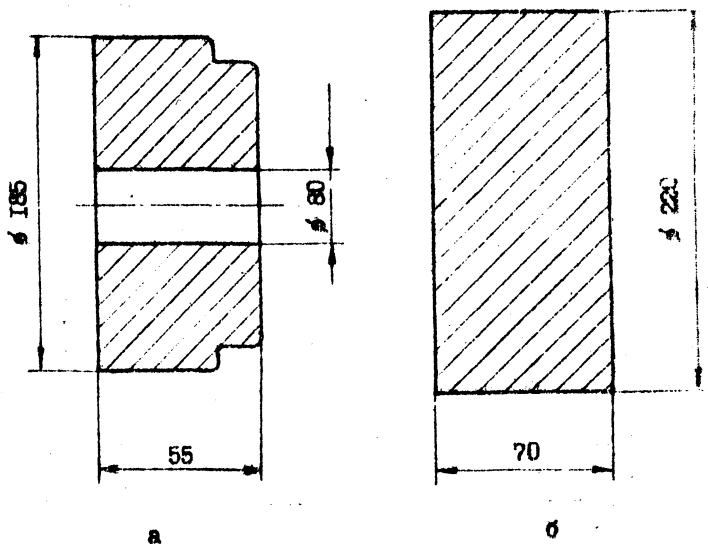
Рис. I. Размеры и форма литых (а) и кованых (б) заготовок
